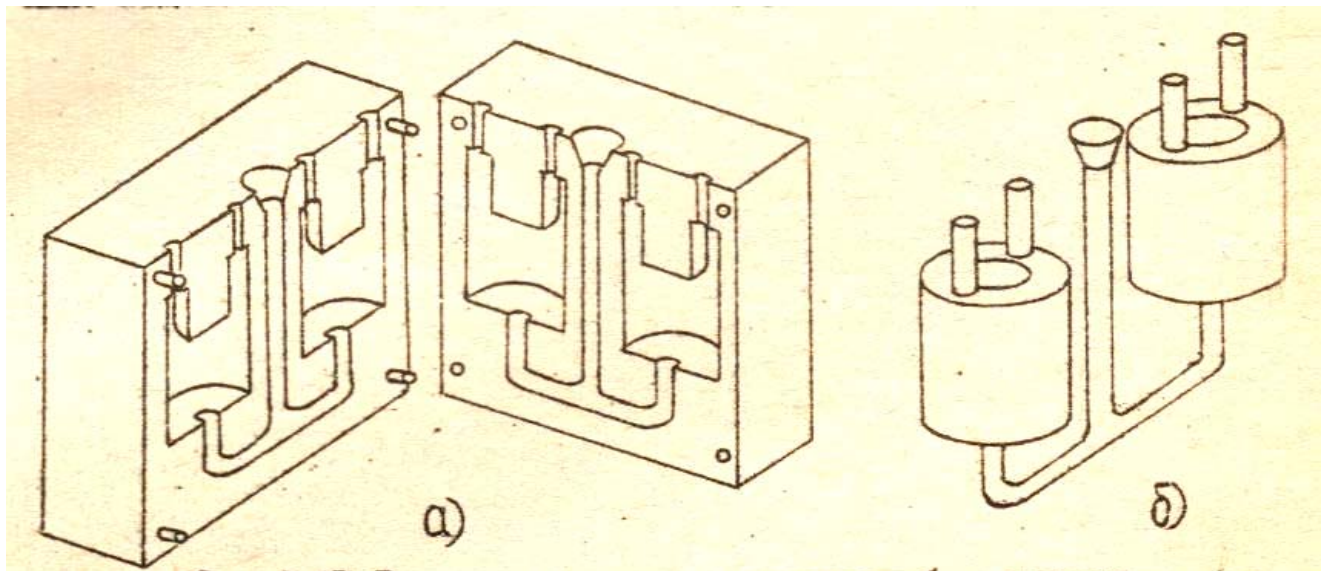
Литье в кокиль: а — кокиль; б — отливка
